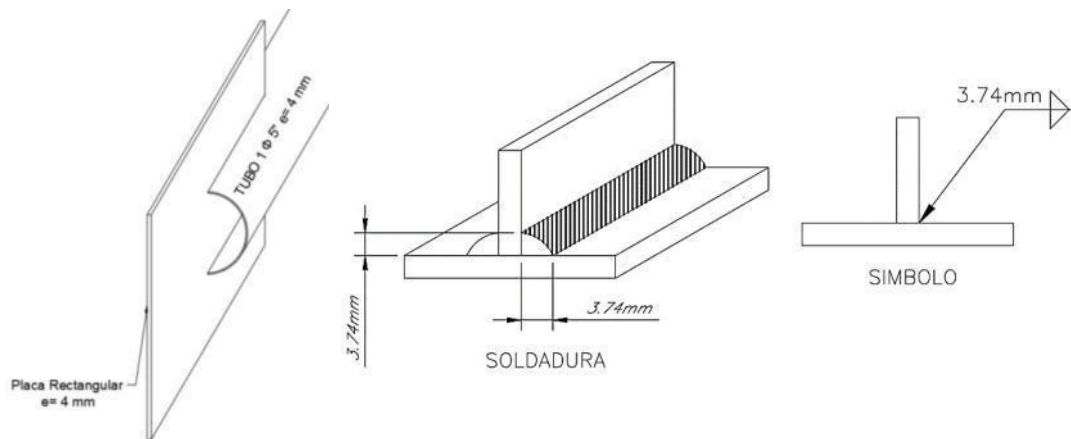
Esquema de soldadura - Placa de unión y Columna (Junta en T con doble filete)
